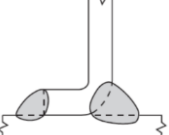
Múltiplos passes ou um só passe de soldadura - [10] Imagem adaptada
